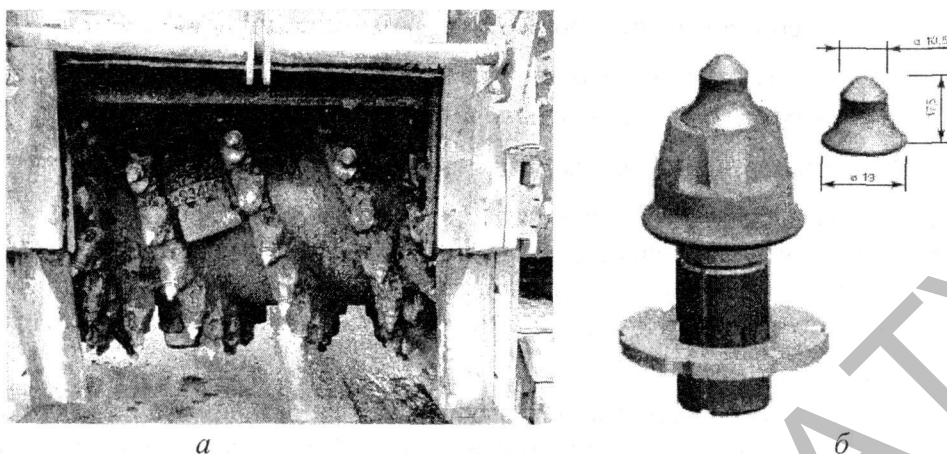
Фотография барабана дорожной фрезы (а) и резца W6 HR для дорожных фрез (x2) (б)
